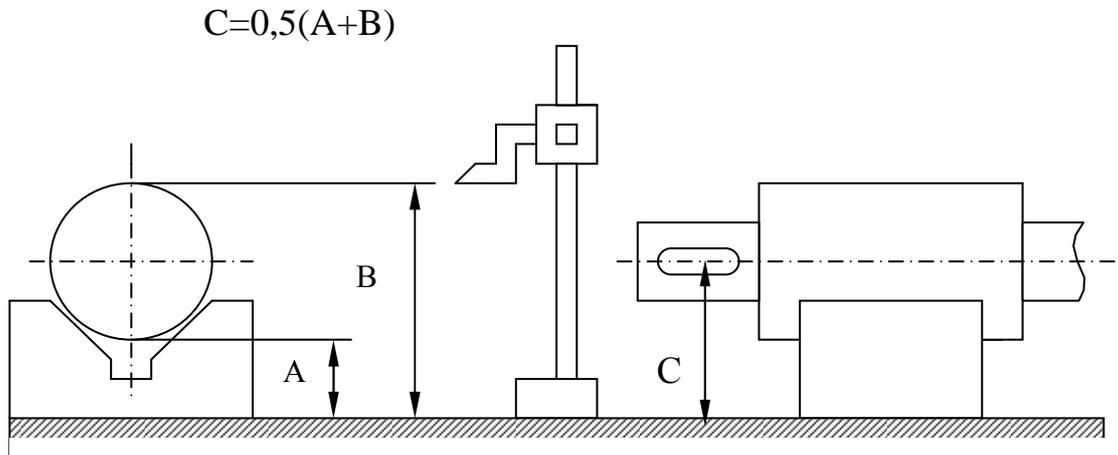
Разметка центровых отверстий и шпоночных канавок
